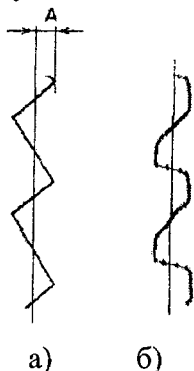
Траектория колебательного движения инструмента относительно заготовки
